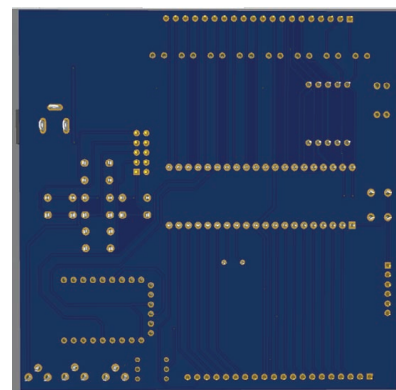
Capa inferior de la PCB en 3D. Elaboración propia.
